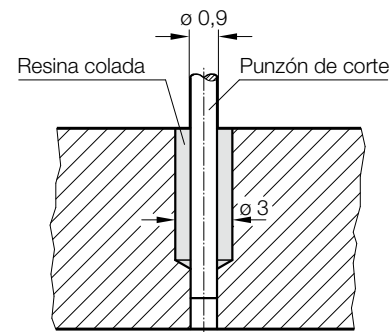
Rellenado de una placa de guía para punzones delgados.
